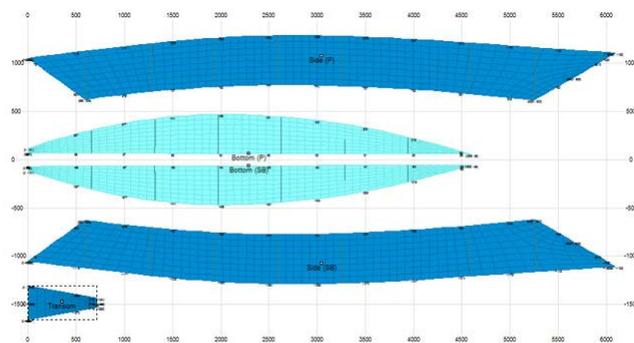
Le plan de découpe sur les plaques de contre-plaqué
